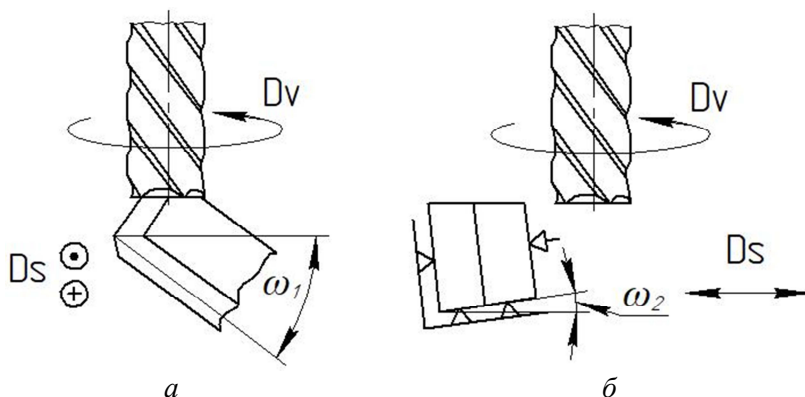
Схема формирования опорной поверхности гнезда под СМП:
